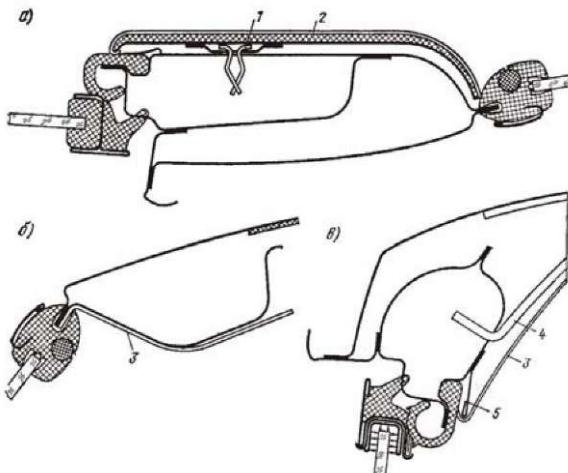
Крепление обивки задней части боковины и обивки потолка:
